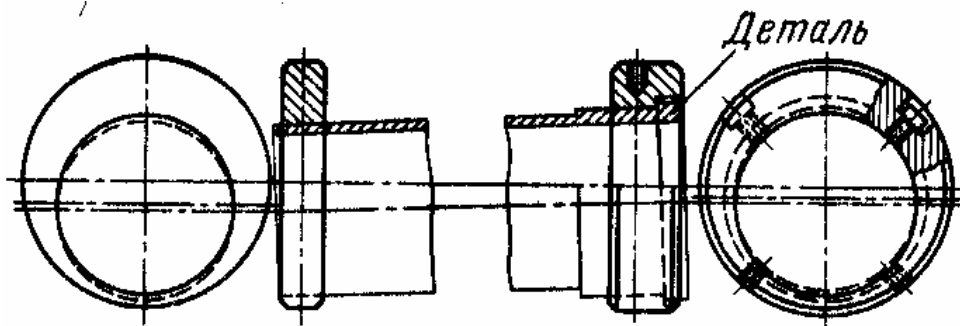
Схема обробки ексцентричної поверхні при установленні заготовки в спеціальних кільцях
